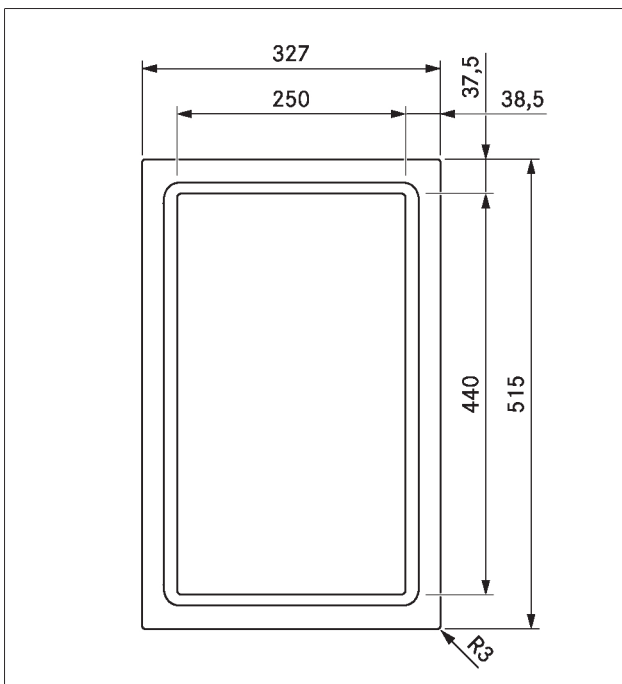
CKT apparatets dimensjoner sett ovenfra
